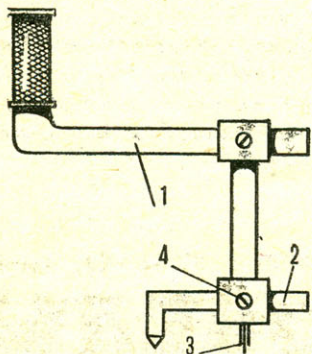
Коловорот для резины: 1 — поворотный рычаг с ручкой, 2 — направляющая штанга, 3 — зажим с лезвием, 4 — винт ползунка.
